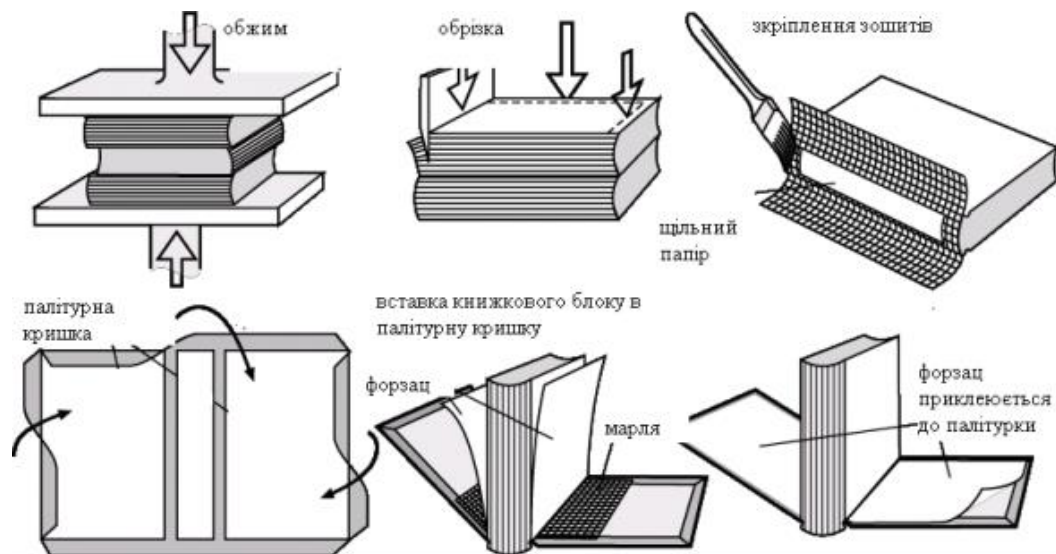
Схема післядрукарської обробки книжки [12]
